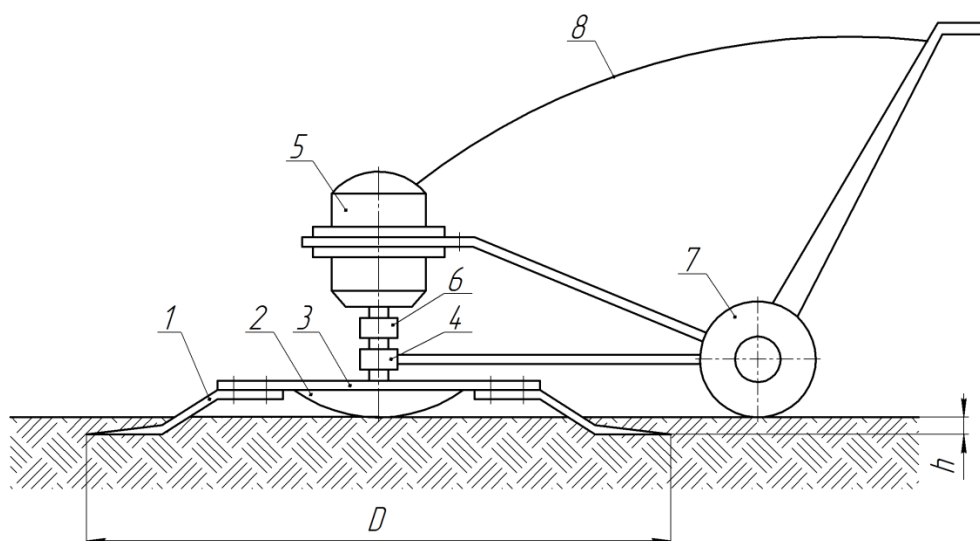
Схема модели культиватора: 1 – рабочий орган; 2 – опорное блюдо; 3 – ротор; 4 – подшипник; 5 – двигатель; 6 – соединительная втулка; 7 – колесо; 8 – тросик газа
